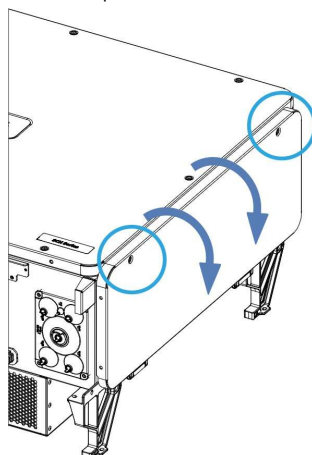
Abra la cubierta lateral de la caja de cables de CA
